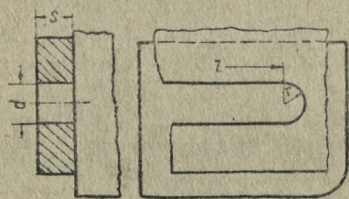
Размеры прорези для увеличения длины сварного шва
